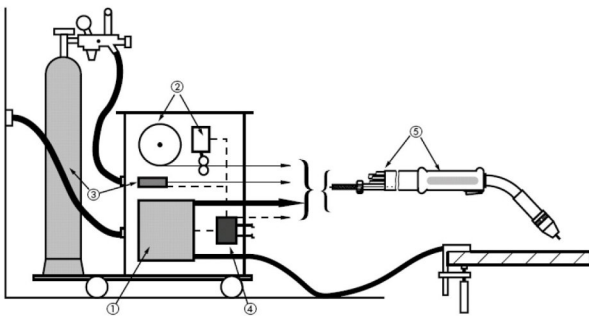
Funktionsprinzip des Schweißgeräts
